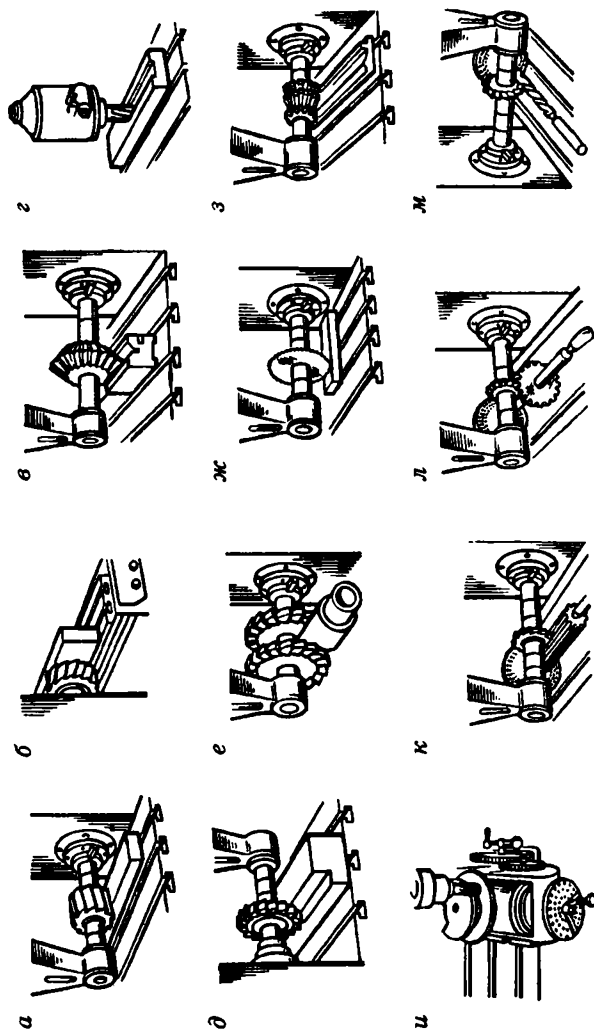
Работы, выполняемые на фрезерных станках:
